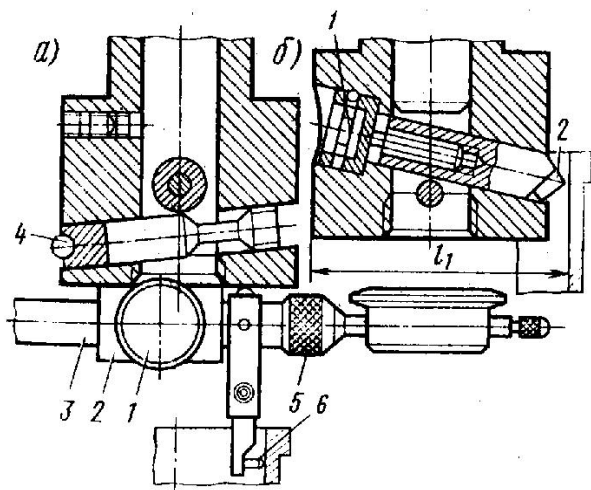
Резцовая головка станка 2А78Н с приспособлениями для центрирования гильз (а) и установки резца (б)
